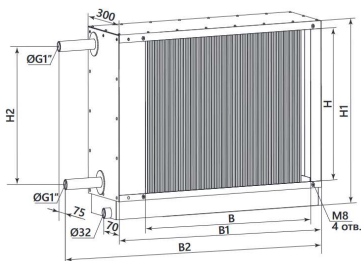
Загальний вид повітроохолоджувача типу С-ВКО
